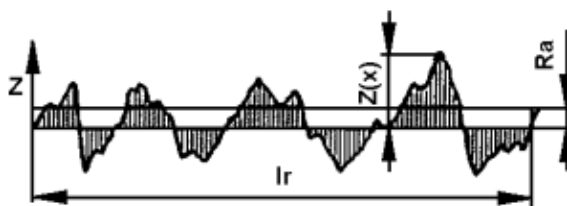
Ilustrace tolerance tvaru plochy [13]
